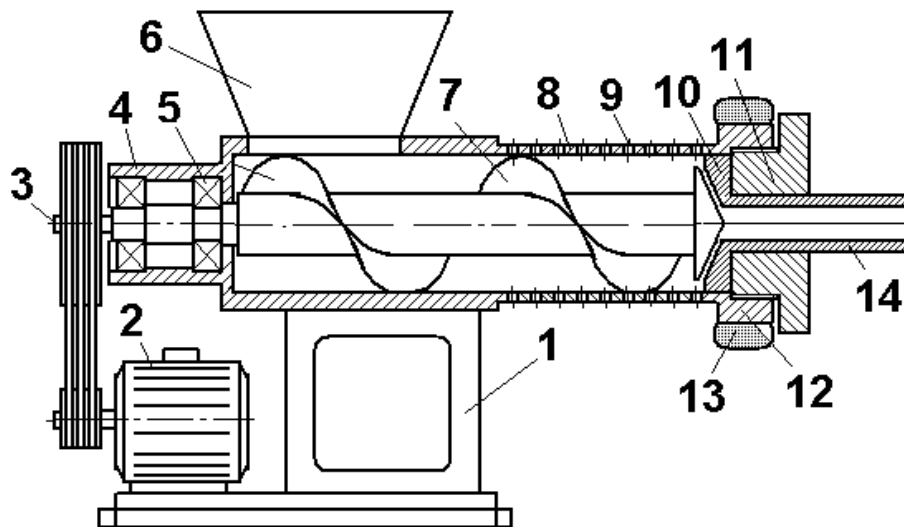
Конструктивно-технологічна схема установки для виготовлення паливних брикетів: 1 – рама; 2 – електропривод; 3 – вал; 3, 4 – корпус; 5 – підшипниковий вузол; 6 – бункер; 7 – гвинт; 8 – перфорована гільза; 9 – отвори; 10 – фільтри; 11 – стакан; 12 – гайка; 13 – електронагрівач; 14 – циліндрична частина фільтри
